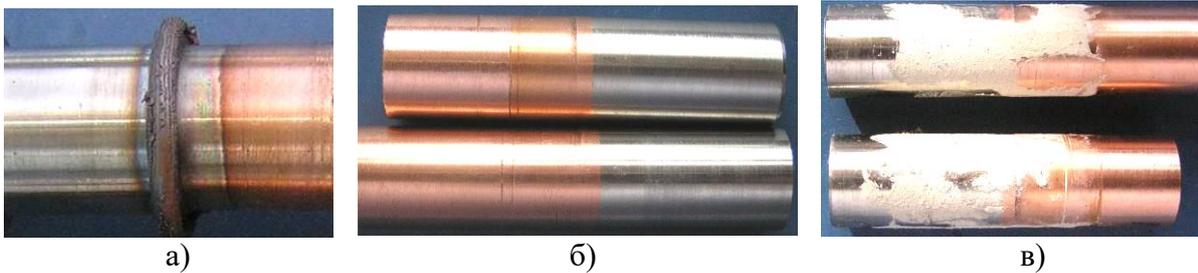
Біметалічні перехідники CuCrZr/НП2/SS316L, виконані ЗТ, – зварний стик (а), зразки після механічної обробки (б) і контролю проникаючою рідиною (в)
